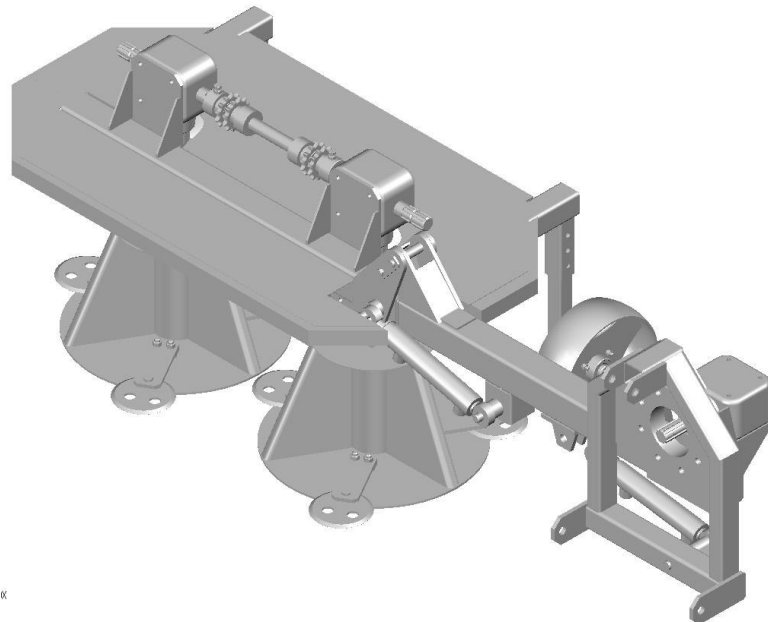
Твердотільна модель ротаційної косарки
